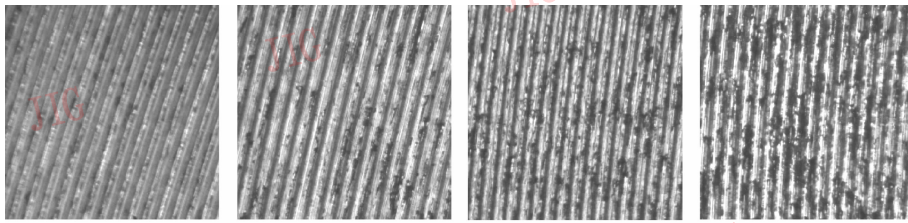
外圆切削加工刀具从锋利到严重磨损的工件图像(实验条件 1)
